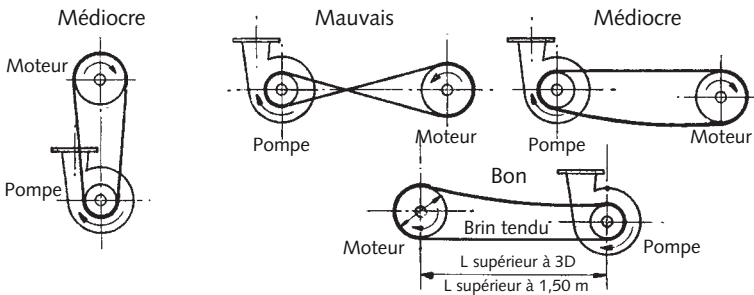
Montage de courroie sur une pompe à axe horizontal
